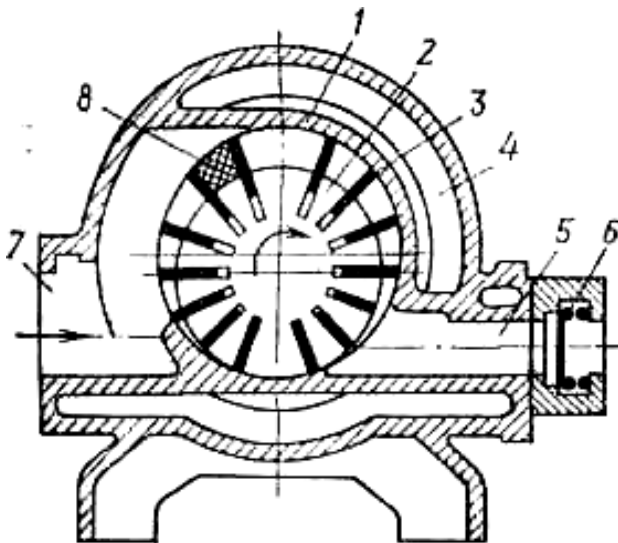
Схеми роторного пластинчастого компресора: 1- корпус; 2 - ротор; 3 - пластина; 4 - сорочка; 5, 7- нагнітальний і всмоктувальний патрубки; 6 - клапан; 8 - камера стиснення
